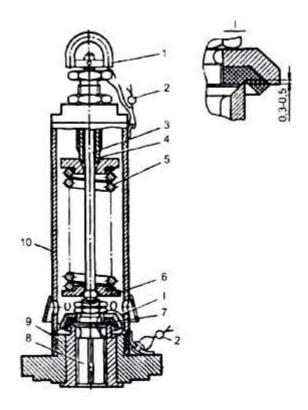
Предохранительный клапан: 1 – рым; 2 – пломба; 3 – шток; 4 – втулка; 5 – пружина; 6 – опора; 7 – клапан; 8 – золотник; 9 – фланец; 10 – крышка
